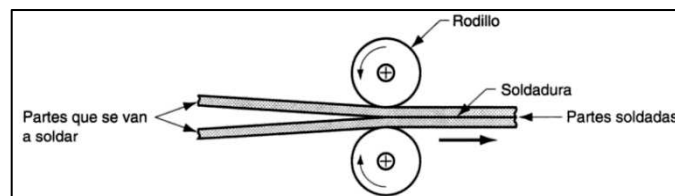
Soldadura por resistencia de rodillo
